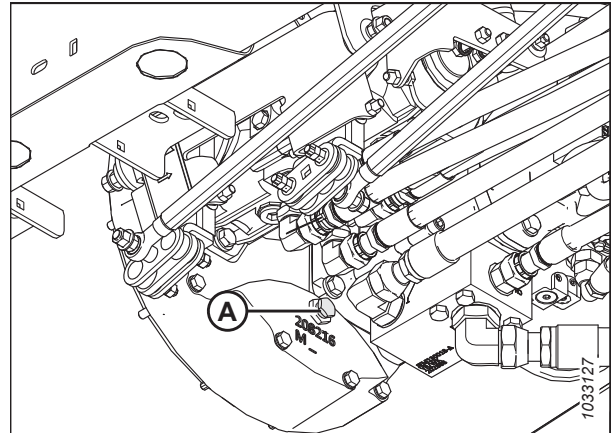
Getriebeschmiermittel-Kontrollschraube
